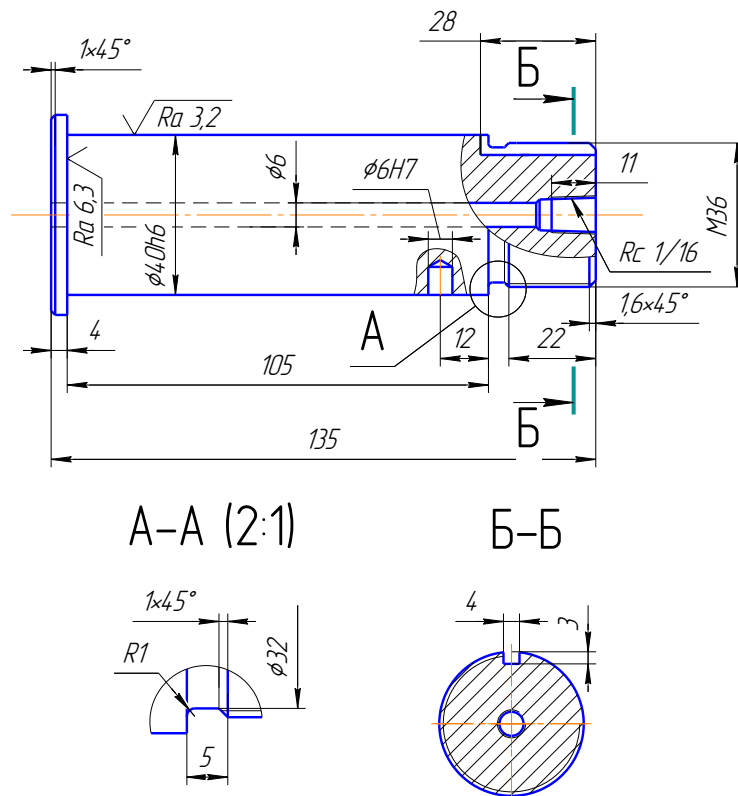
Робоче креслення осі опорного котка каретки
